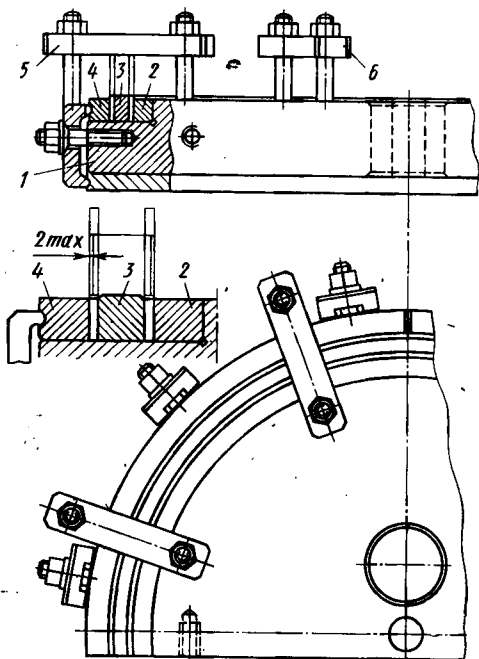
Приспособление для сборки бандажей с лопатками под сварку
